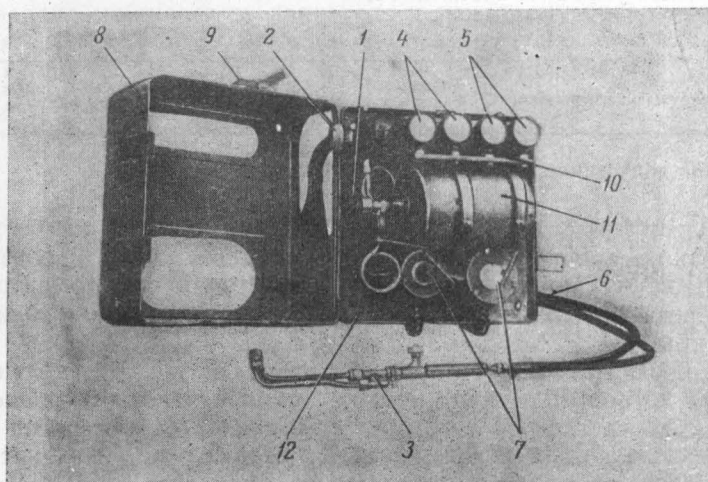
Ранцевая установка РУ для газовой резки стали:
